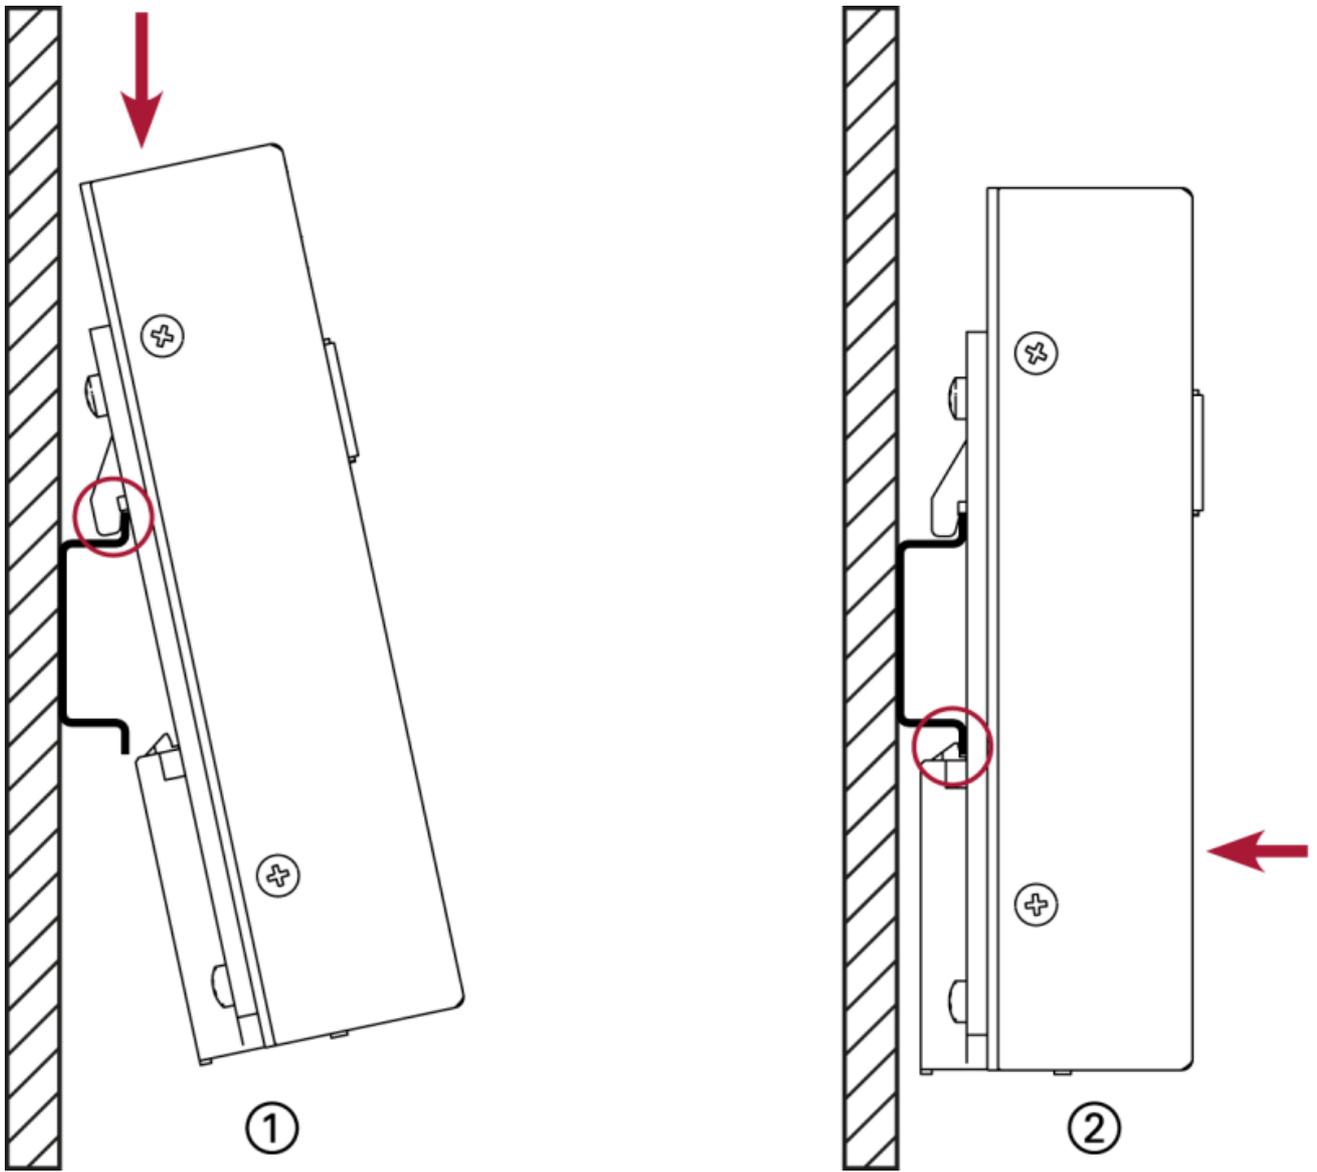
Крепление контроллера на DIN-рейку
